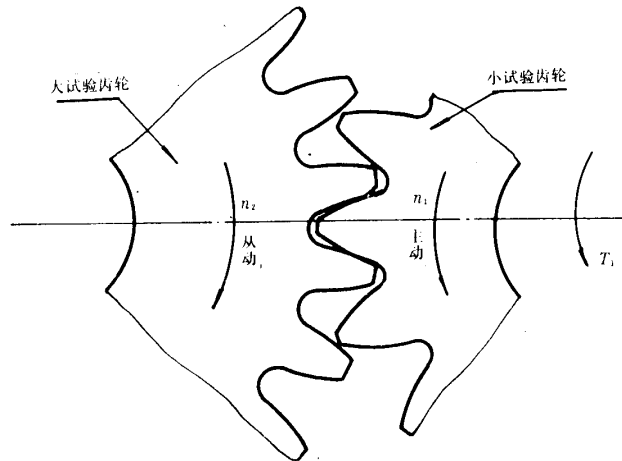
试验齿轮的安装和转向(从试验齿轮箱端向电动机观察)
